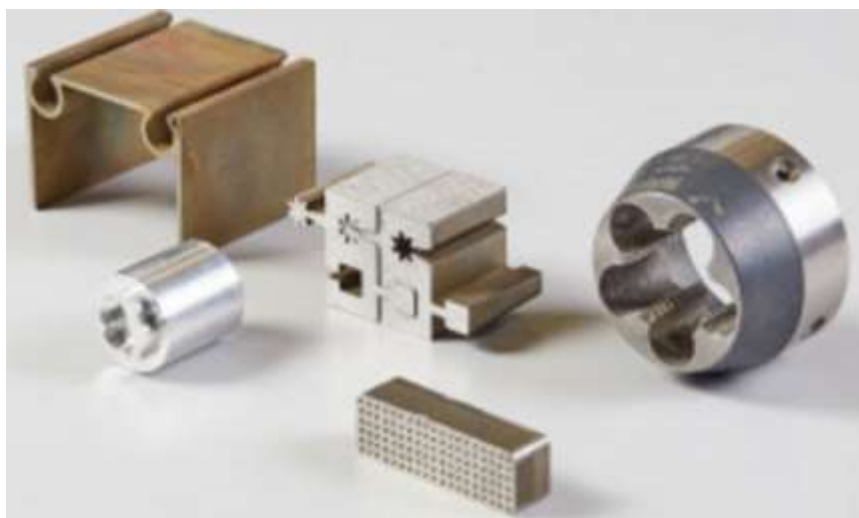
Пример выполненных деталей сложной формы на малогабаритном фрезерном станке
